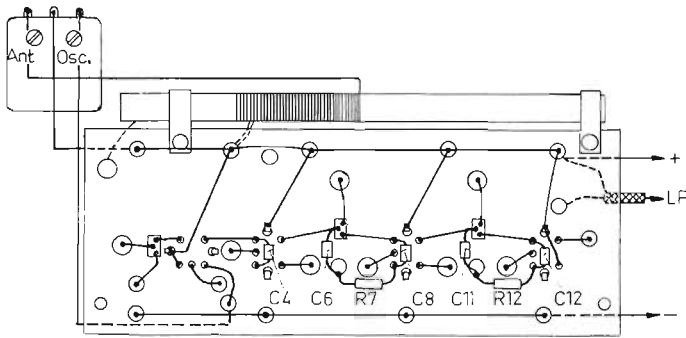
Ledningsmönstret på plattans undersida mellan de olika lödstiften.
